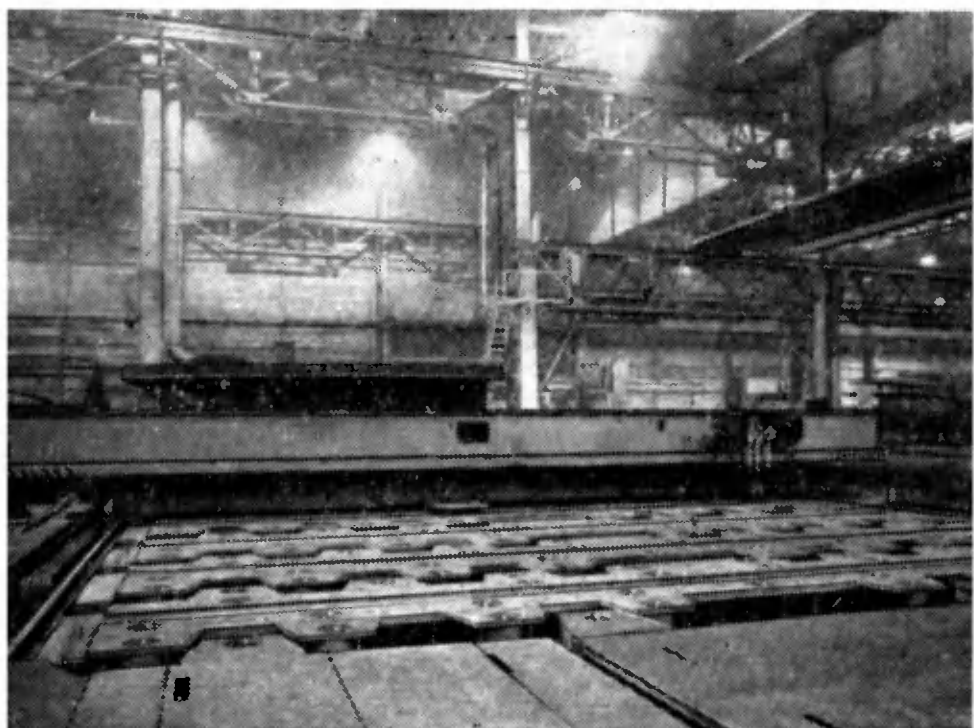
Сварочный портал и балки с флюсомедными ручьями линии полотнищ Выборгского судостроительного завода.
